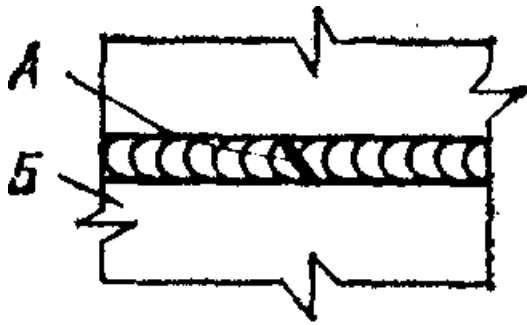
Поперечная трещина А в сварных швах стенки резервуара
